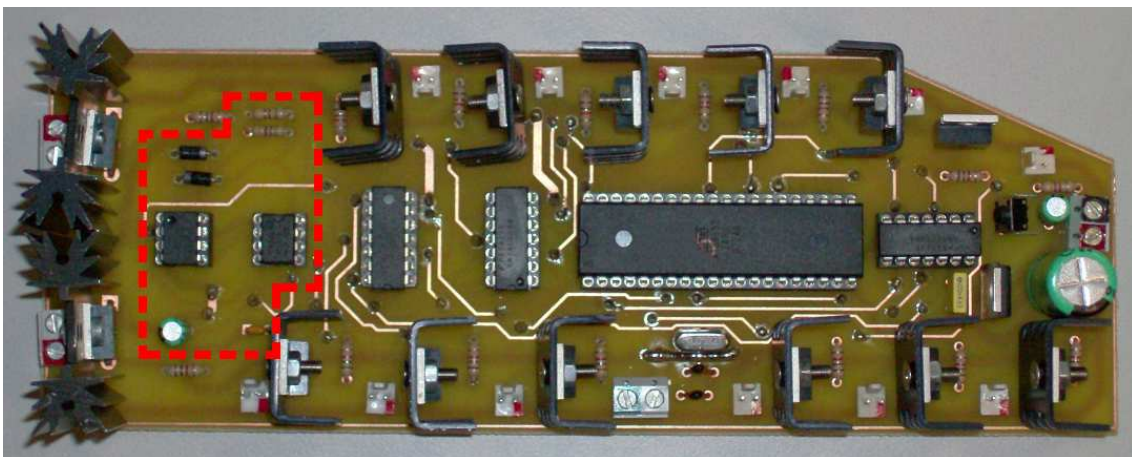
Disposición del integrado LM555 y componentes pasivos en la placa PCB, encuadrado en rojo.
